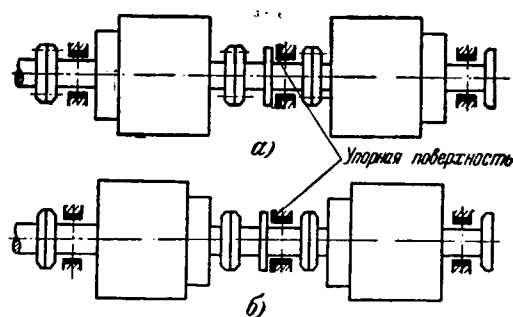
Конструкция двухъякорного двигателя с промежуточным соединительным валом и внутренним упорно-опорным подшипником.
